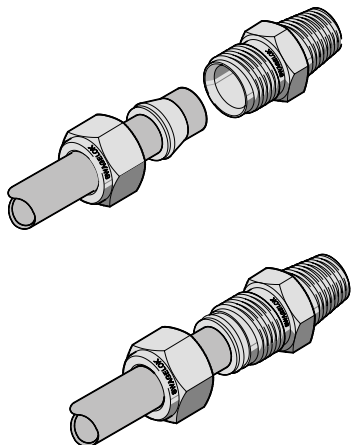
Установка предварительно обжатого узла в корпус фитинга
